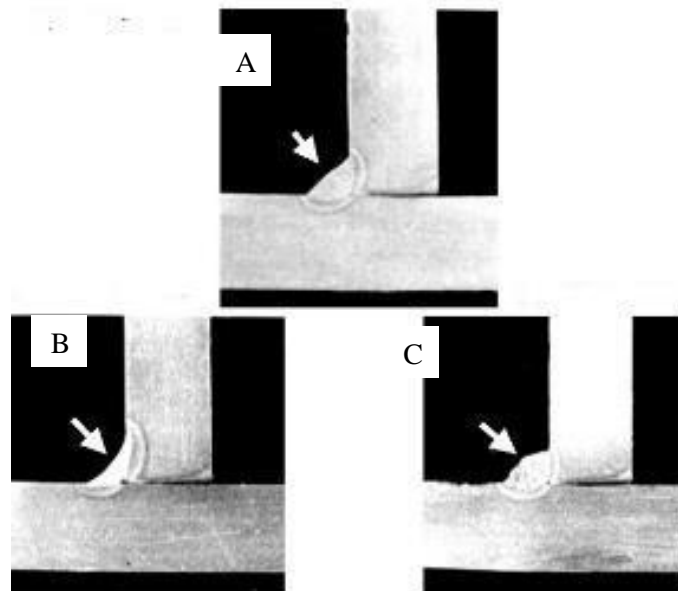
A. Buena soldadura de filete. B. Soldadura de filete cóncavo. C. Soldadura de filete convexo.
